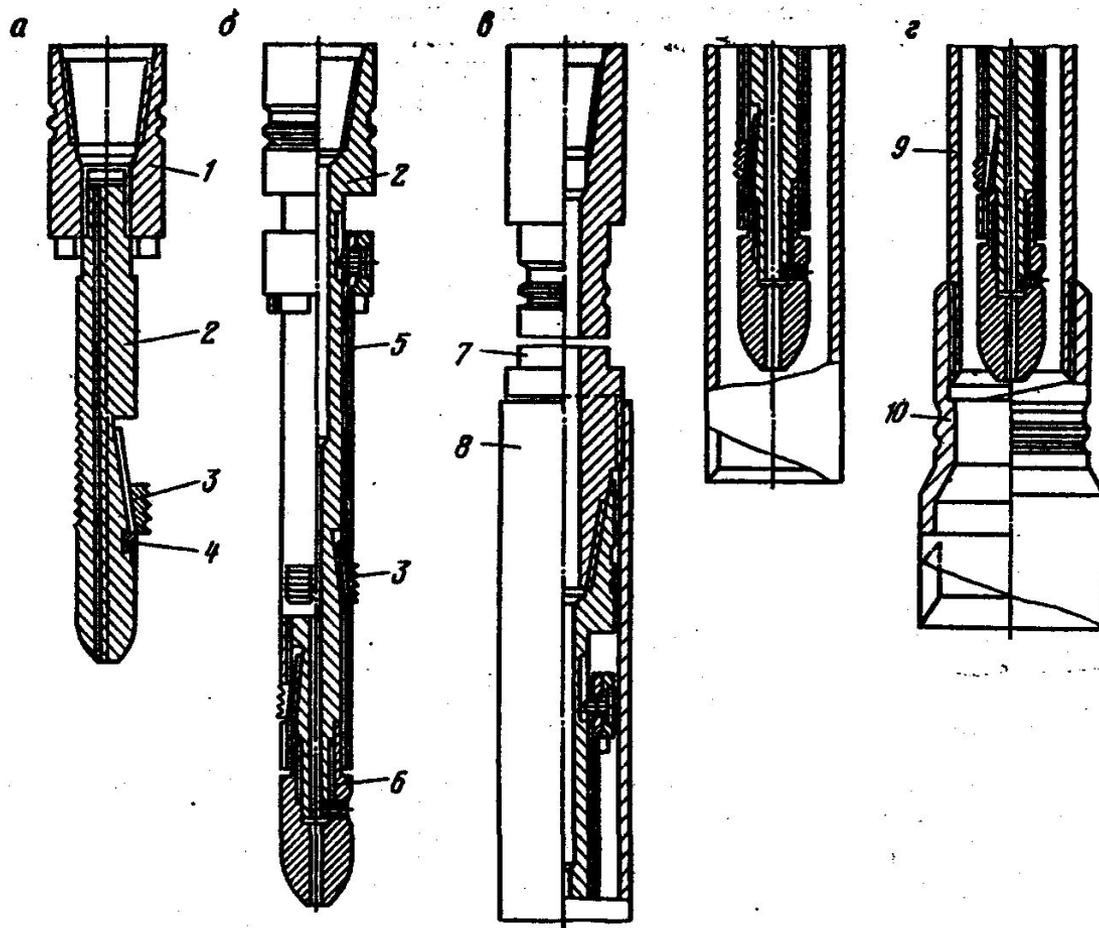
Труболовка внутренняя неосвобождающаяся ТВ:
